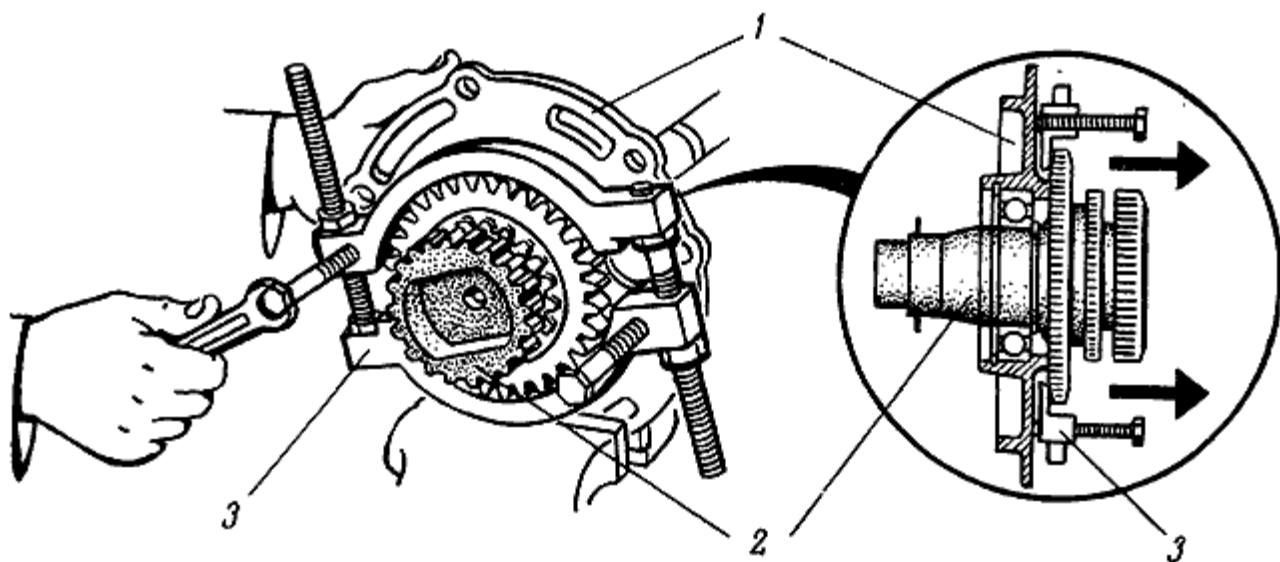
Спрессовка опорной крышки с вала сцепления:
